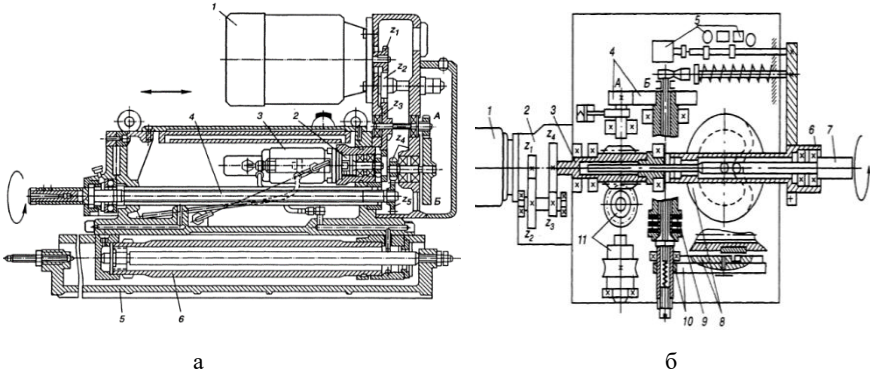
Силкові головки агрегатних верстатів: а – з пересувним корпусом; б – з подачею пінолю
